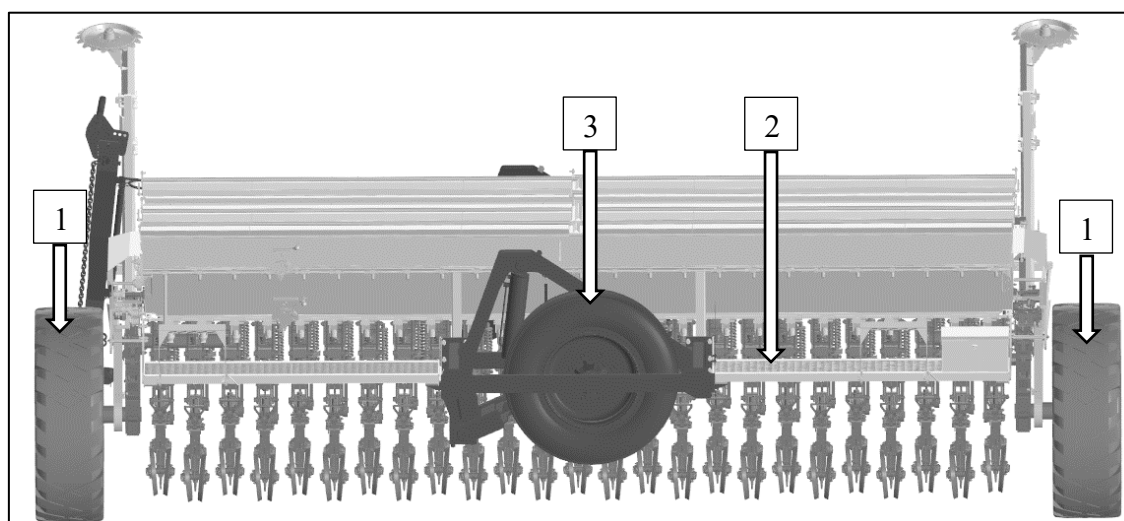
Вид сзади: 1 – колёса опорно-приводные; 2 – площадка для доступа к бункерам сеялки; 3 – колесо механизма боковой транспортировки
